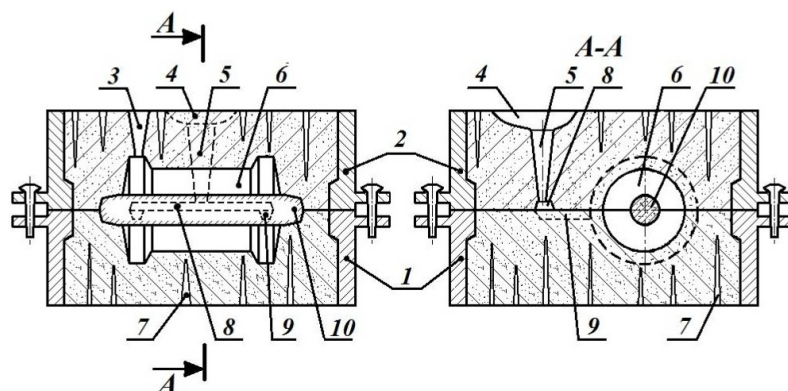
Эскиз разреза песчаной формы для отливки стальной втулки:
